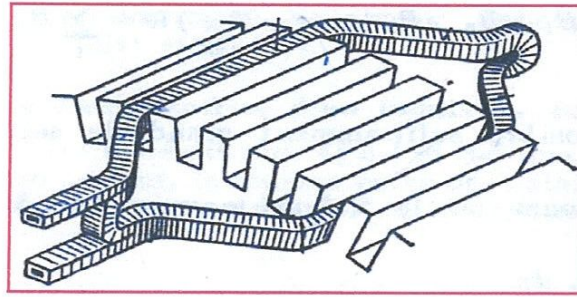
Disposition d'une section de l'enroulement d'un induit. [1]
